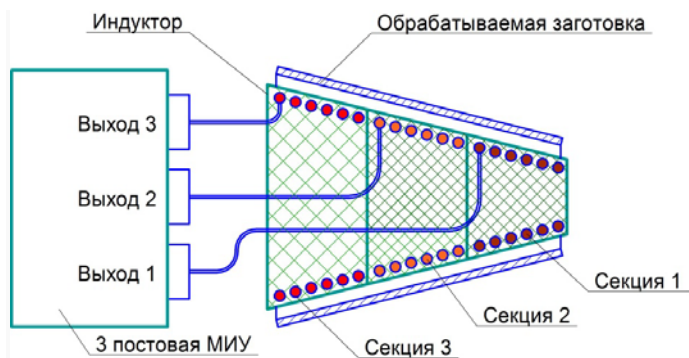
Технологическая схема обработки крупногабаритной заготовки
